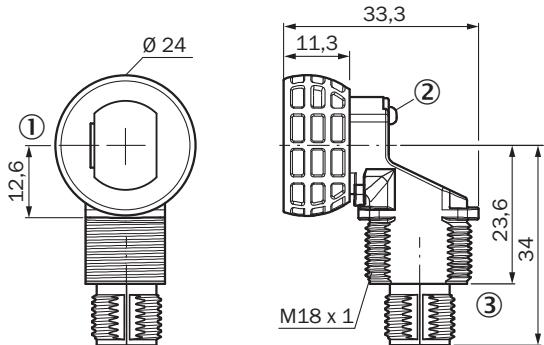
ZSE18-5xxxxx/ZSE18-Exxxxx, M12-Steckverbinder
